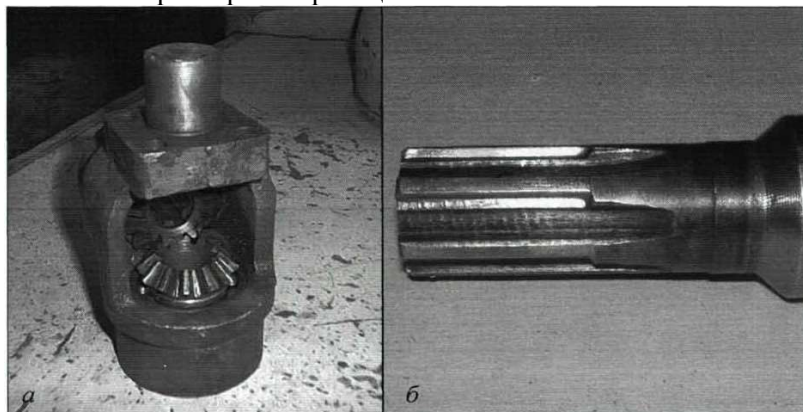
Конический редуктор механизма привода масляного насоса в сборе 700А.17.01.290 (а) и шлицевая часть вала привода насоса 700А.17.01.191 (б)
